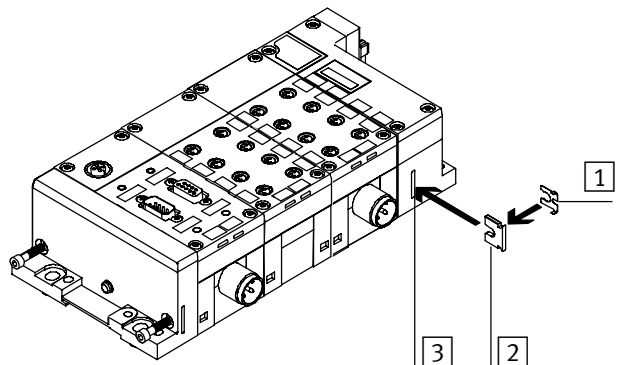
/6: Befestigungs- und Sicherungsblech im Pneumatik-Interface
